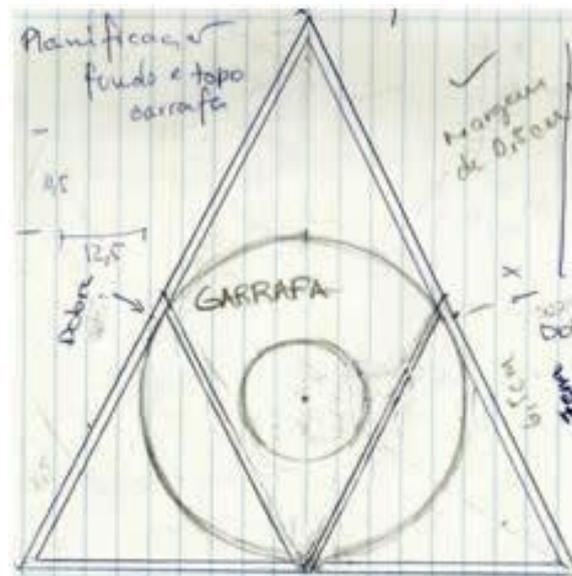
Esboço de planificação da garrafa e embalagem - Planta.
